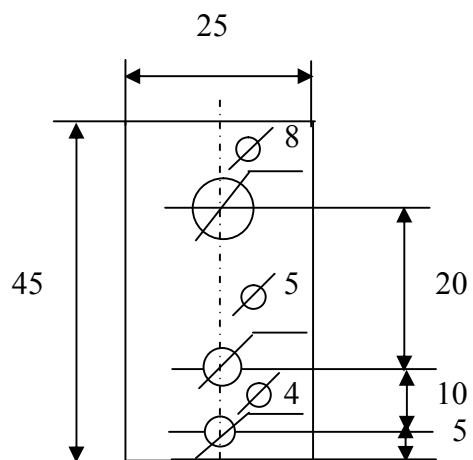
Установочные размеры индикаторного блока УПН-КЛ
